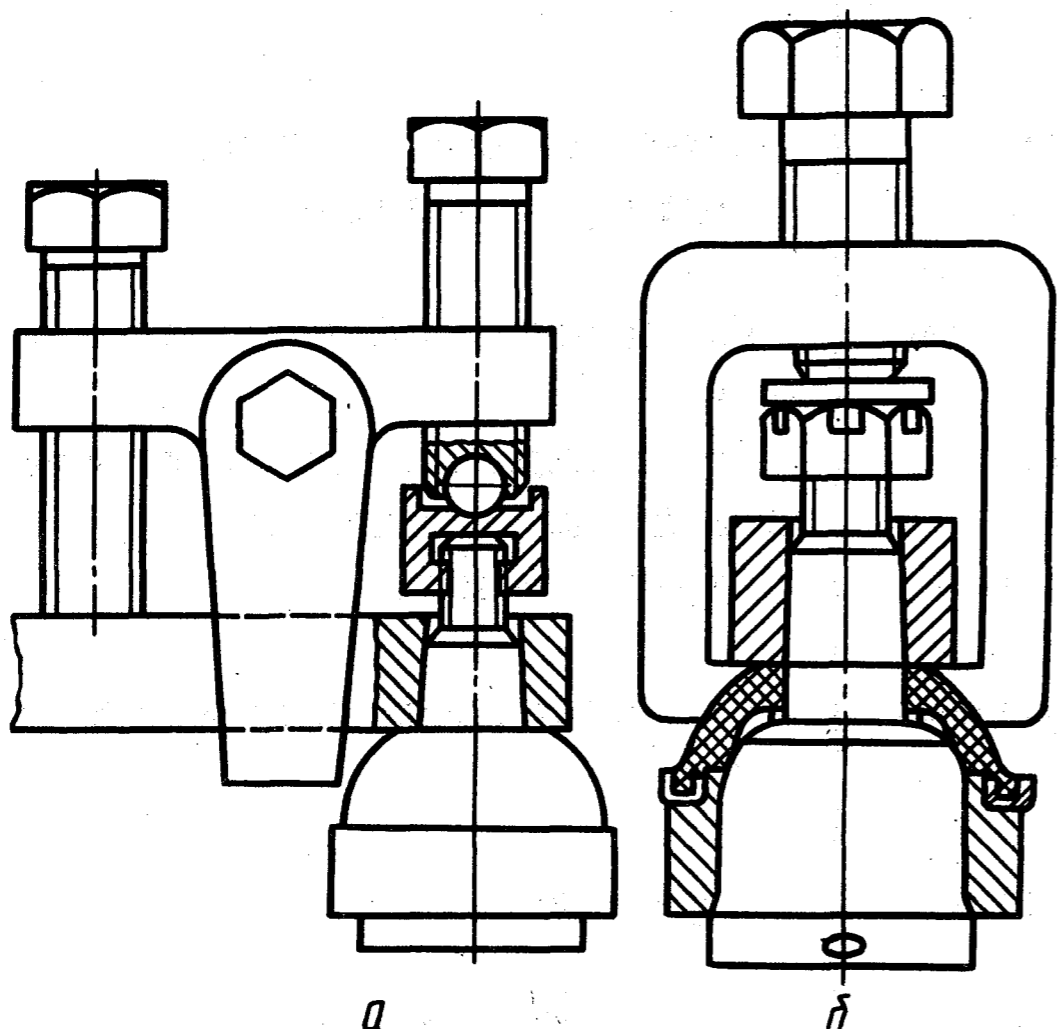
Выпрессовка пальца шарового шарнира рулевых тяг:
